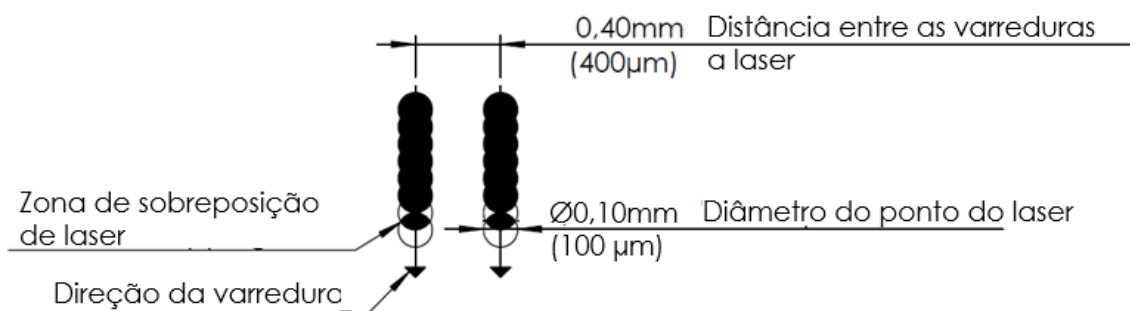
Região da Superfície que foi irradiada a laser (dimensões em milímetros)
